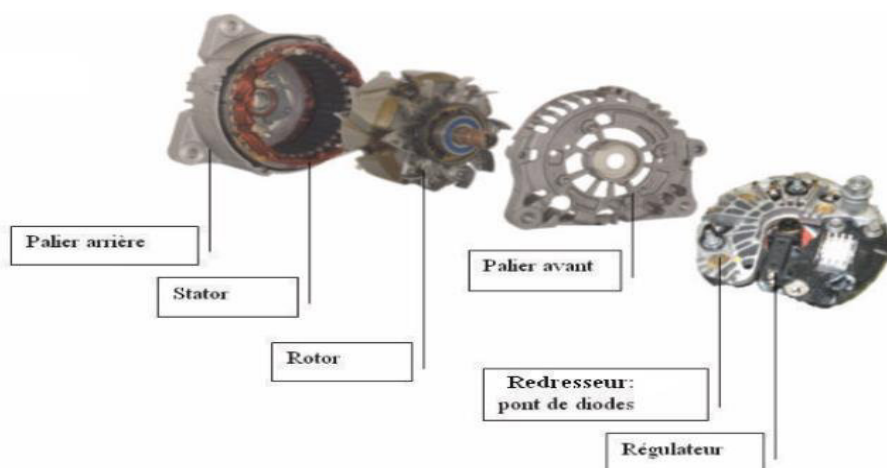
Vue éclatée d'un alternateur à griffes [15]
